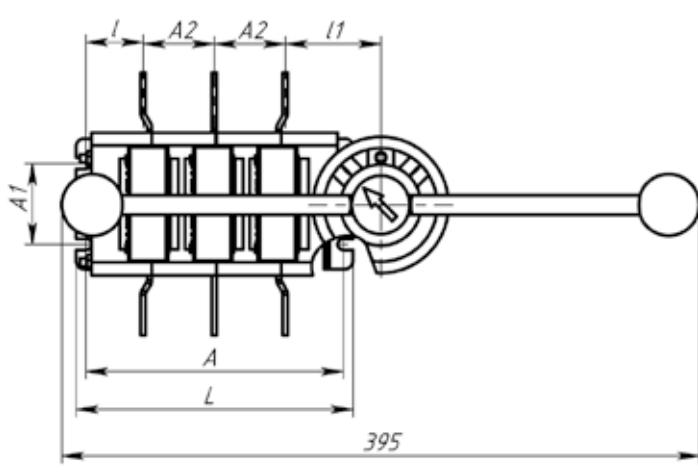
Выключатель-разъединитель на два направления трехполюсный с передней поворотной рукояткой
